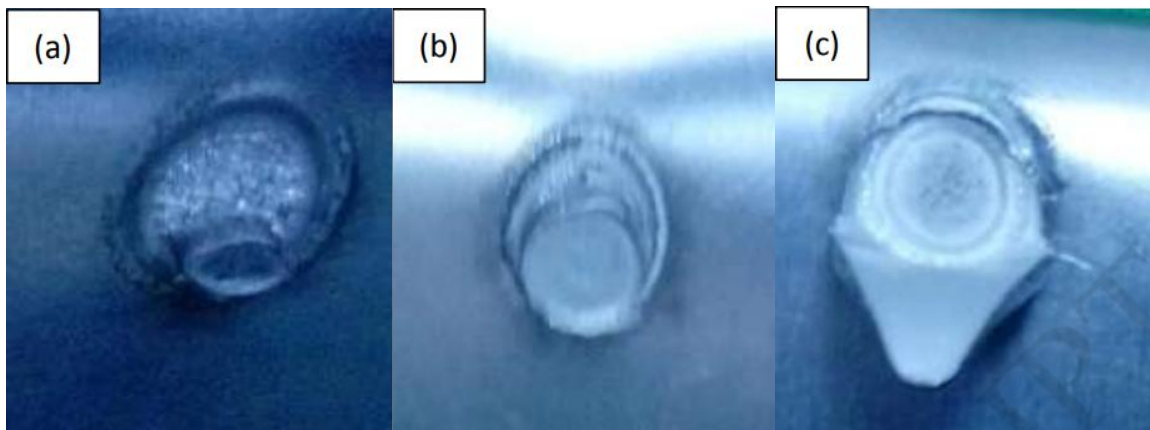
Макроскопия разорванных точечных соединений сварки:
